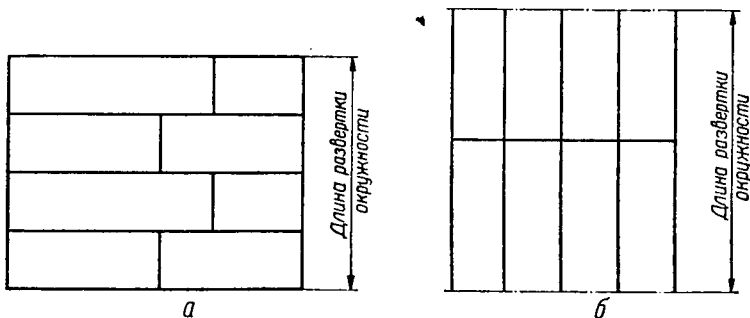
Схема расположения сварных швов свальцованных карт.
